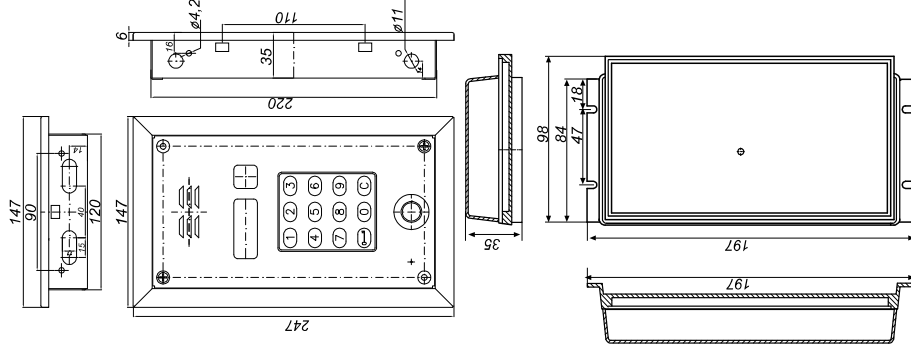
Габаритные размеры деталей домофона типа SA-3500
